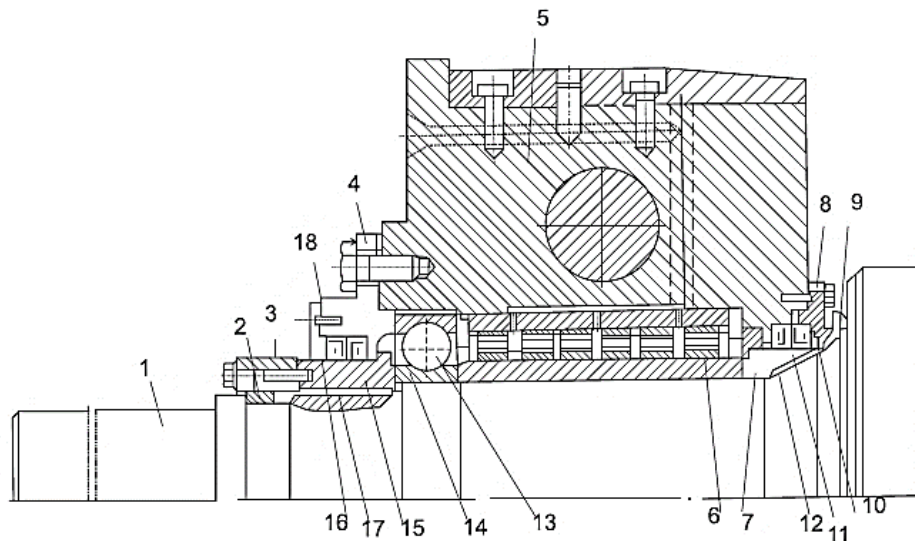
Валкова опора робочого валка стану 1200 холодного прокатування
